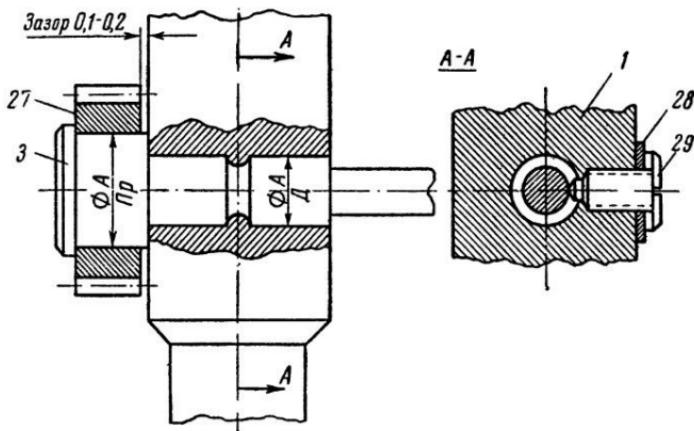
Модель механизма подачи суппорта токарного станка (узел крепления «шпинделья»): 1 — стойка; 3 — «шпиндель»; 27 — ведущее зубчатое колесо «шпинделья»; 28 — шайба; 29 — стопорный винт.
